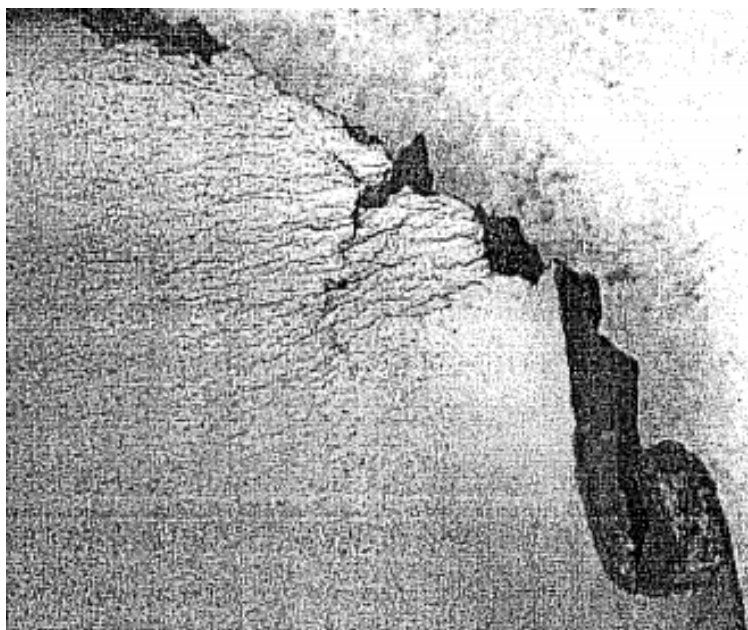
Внешний вид входной кромки лопатки близи излома
